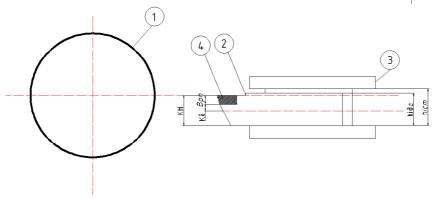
Схематичный окончательный вид после подбора кортежей. 1 – заготовка, 2 – $Д\Gamma$, 3 - резцедержатель станка, 4 – $P\Pi$
